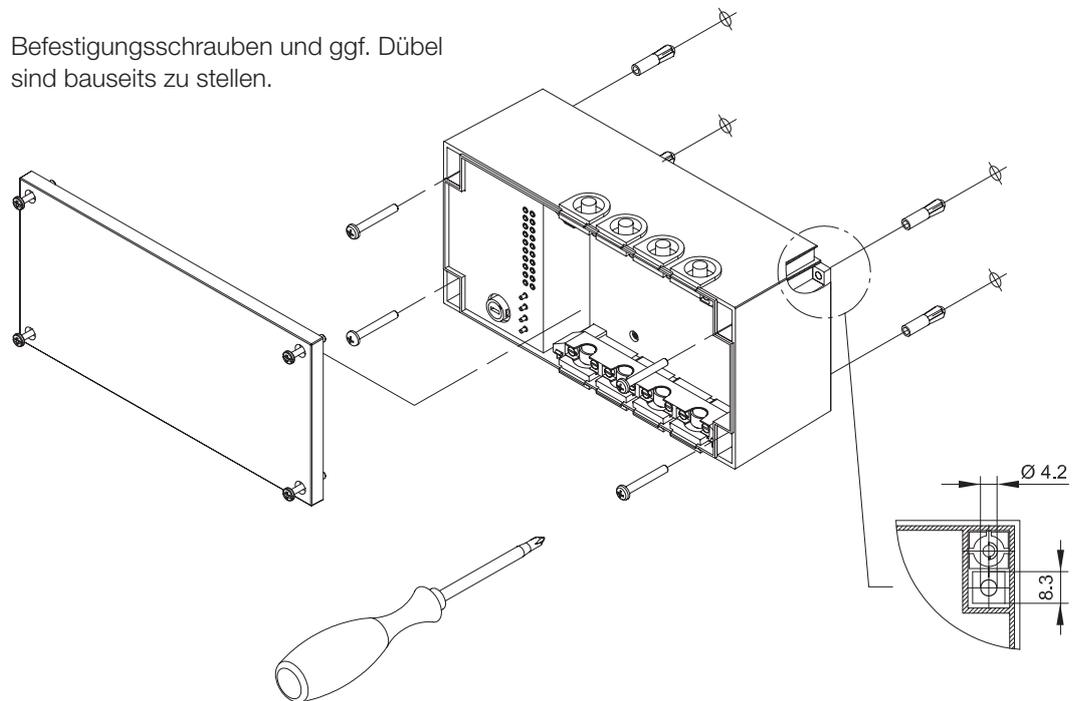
Bohrplan für Montage BS2-IO-01 ohne Montagelaschen
